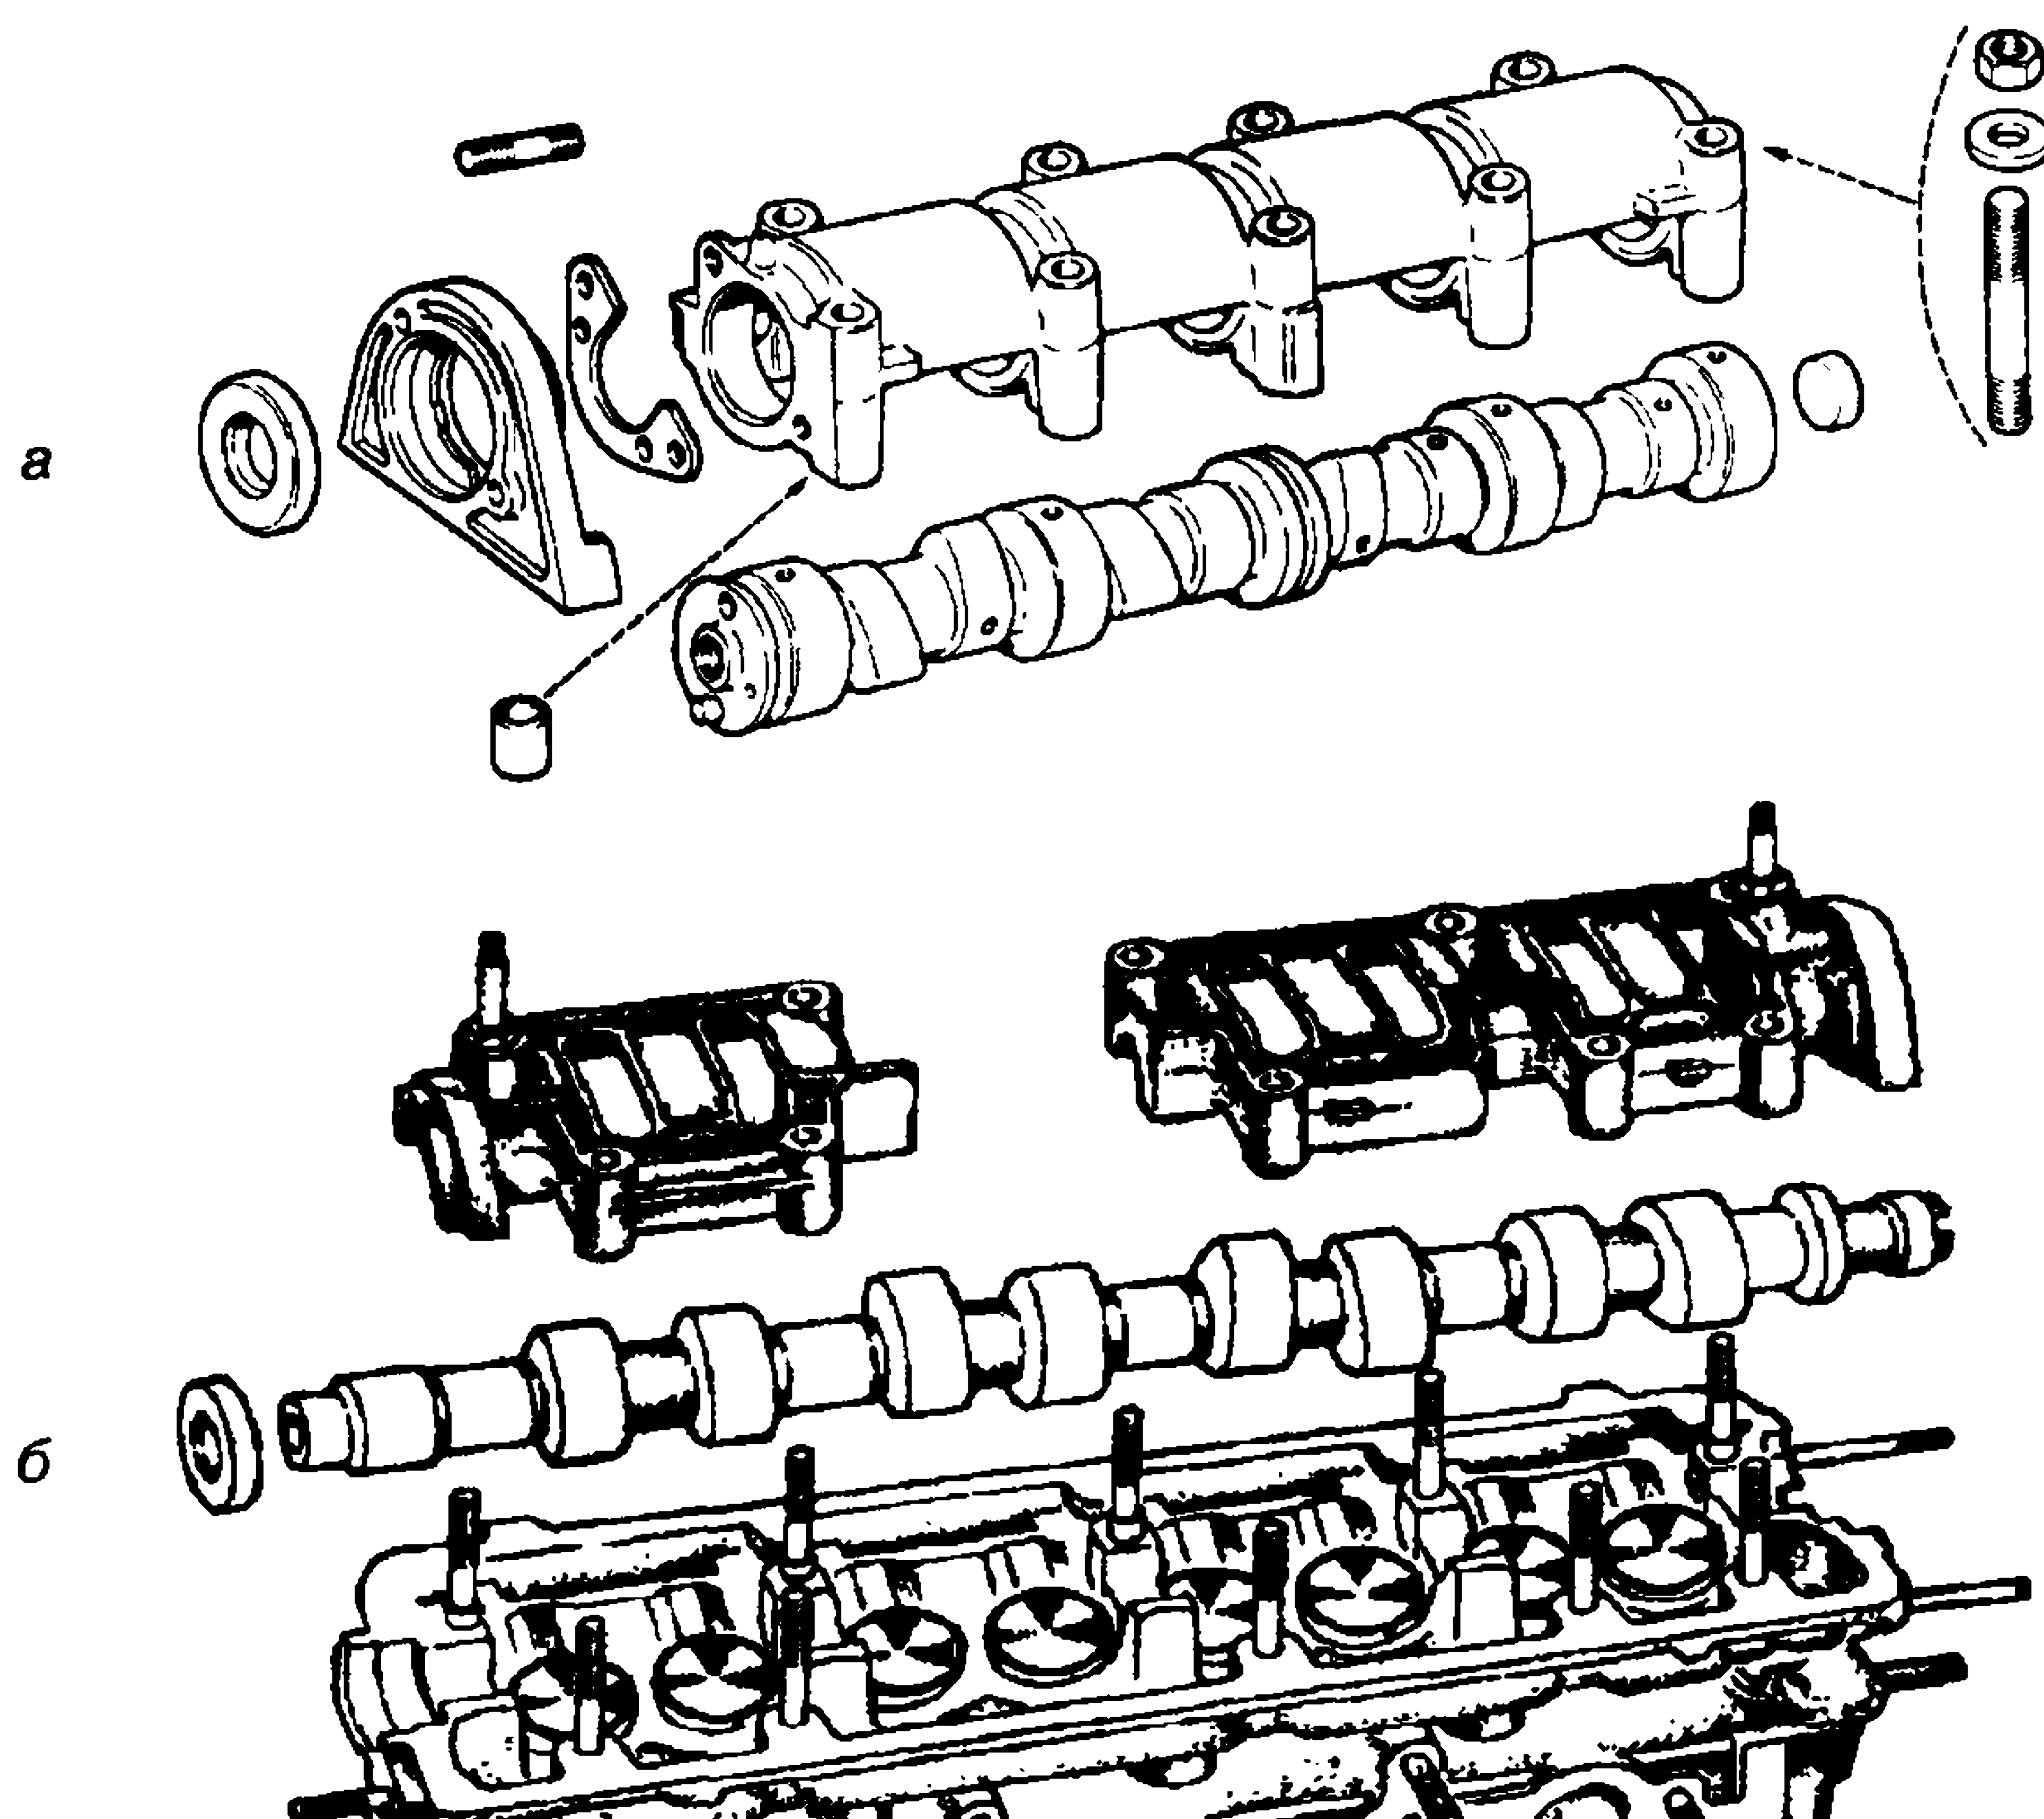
Установка распредвала двигателей с цепным приводом и двигателя 2105 (держатель с сальником только у двигателя 2105) (а) и распредвала двигателей 2108, 21081, 21083, 2110, 2111, 2112 (б)
